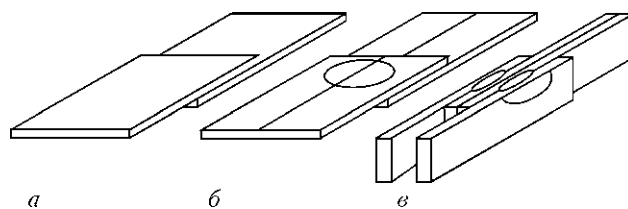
Схема подготовки сварных образцов к изготовлению микрошлифов: а — перед сваркой; б — после сварки с линией разреза вдоль сварной точки; в — для изготовления микрошлифа
